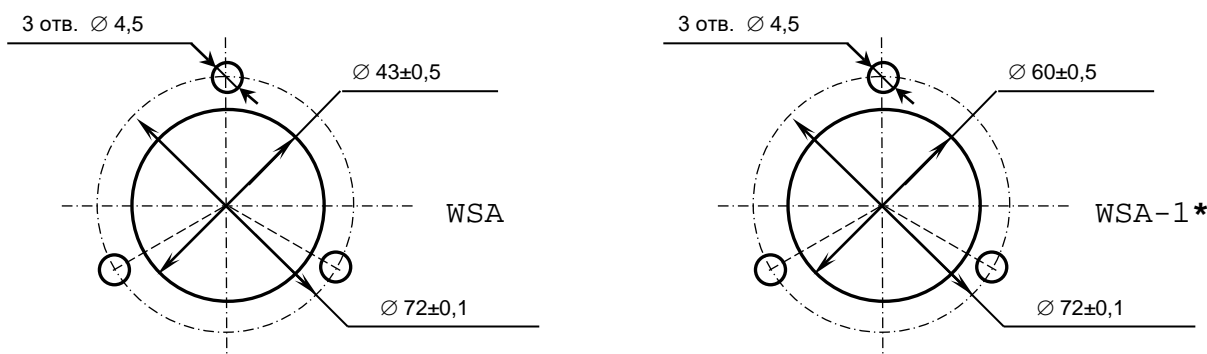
Установочные размеры штурвала WSA и WSA-1
